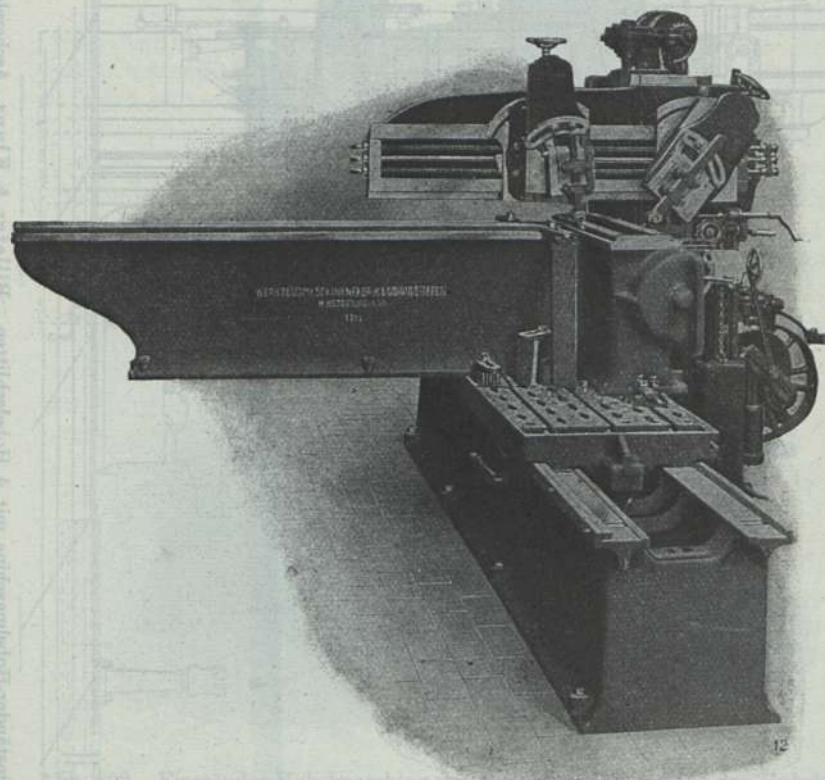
Einständer-Hobelmaschine. H. Hessenmüller, Ludwigshafen.
